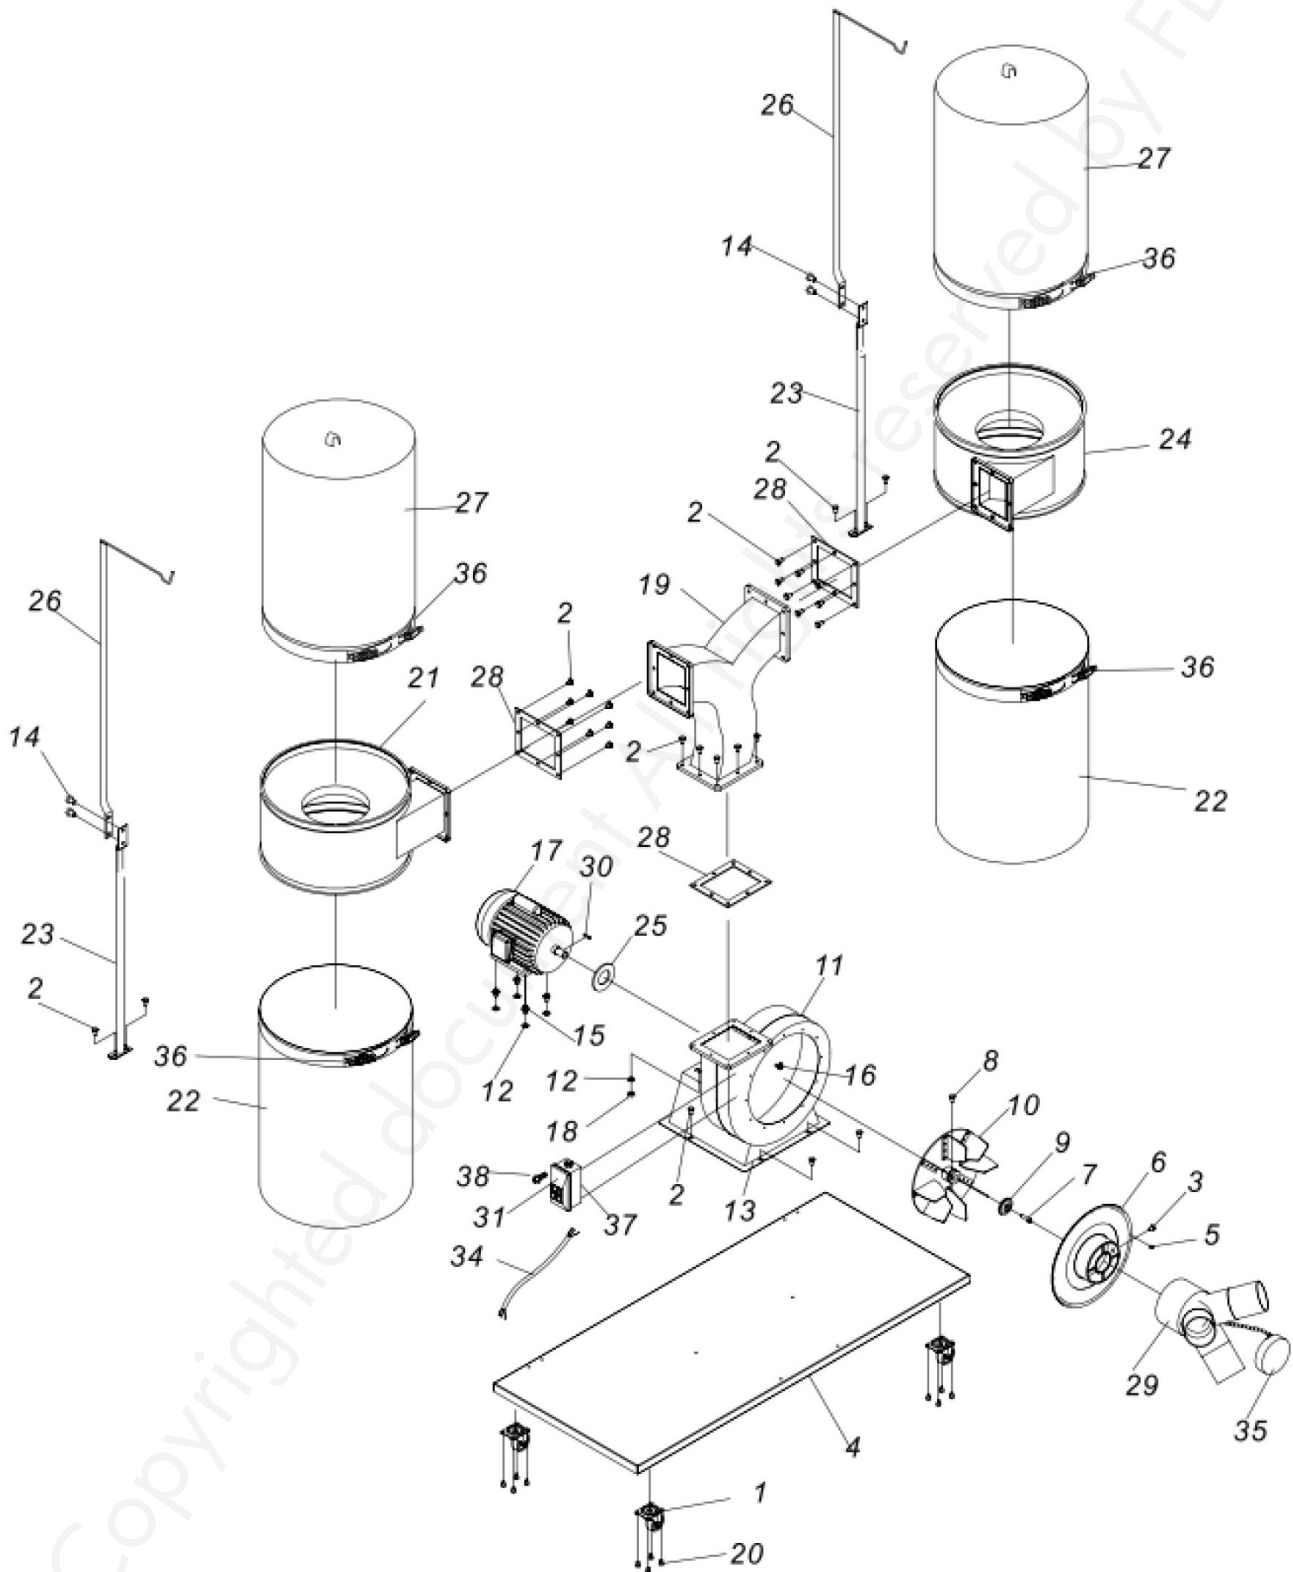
Opengewerkte tekening 2 - SAA 3001/3003
